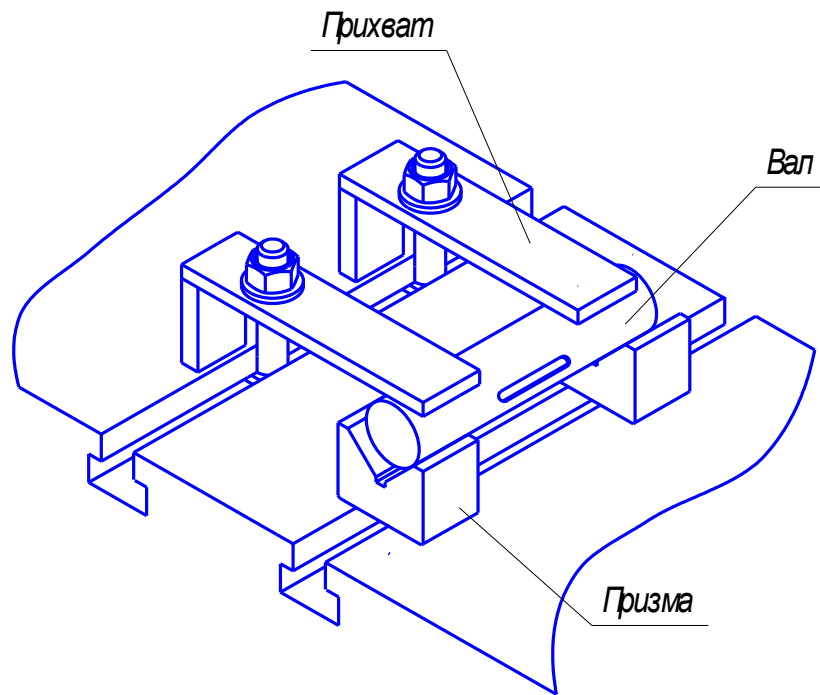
Закріплення заготовки в призмах на столі фрезерного верстата
